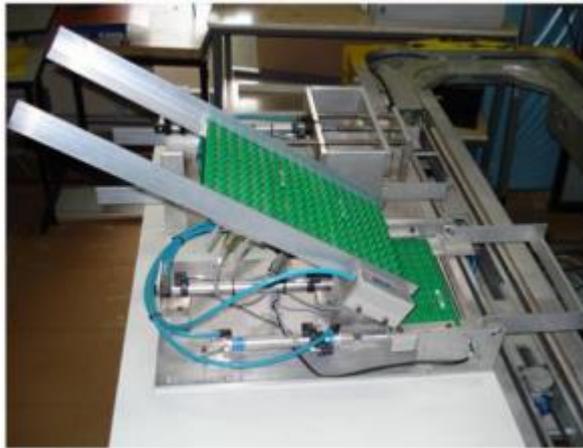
Posto de carregamento. Fonte: SILVERIA JUNIOR (2016)
